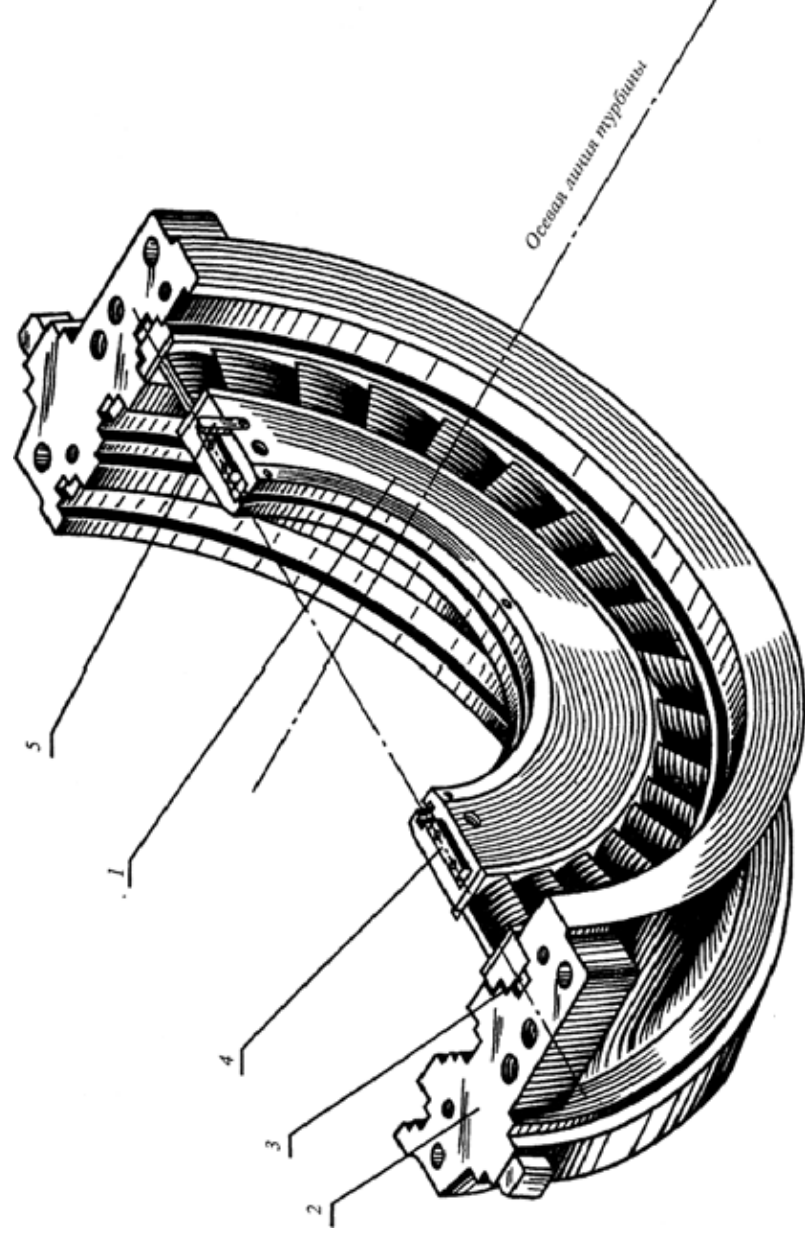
Установка сварной диафрагмы в обойму: 1 – диафрагма; 2 – обойма; 3 – подвеска диафрагмы; 4 – продольная шпонка; 5 – поперечная шпонка
